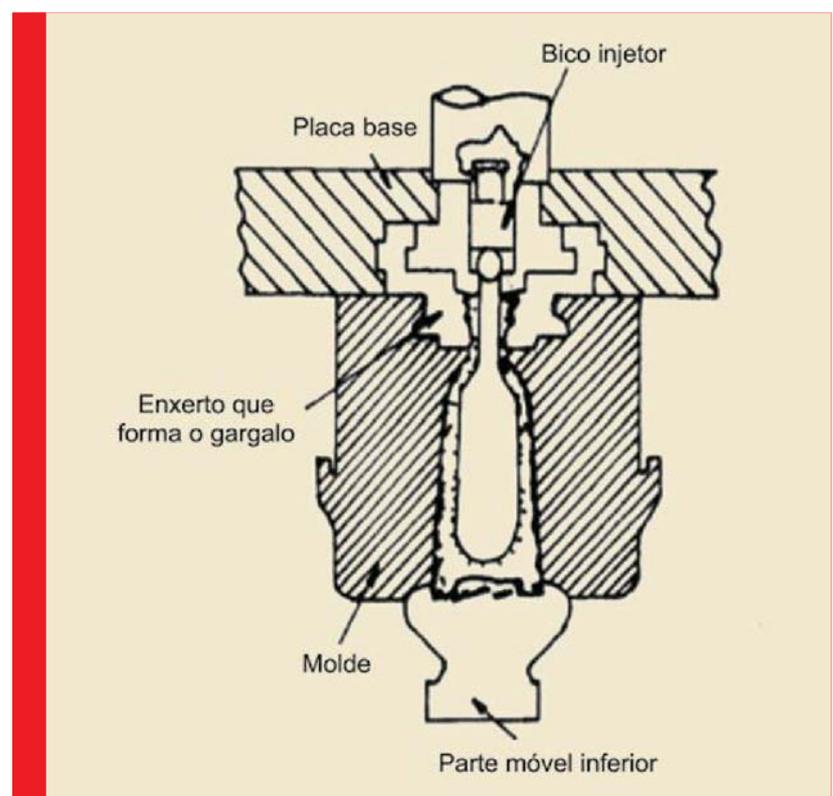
Processo de moldagem de frascos e garrafas por sopro^[1]
